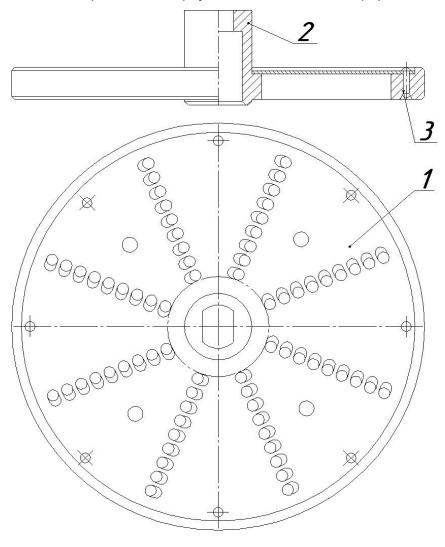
Диск шинковочный: 1 – диск шинковочный, 2 – корпус, 3 – заклепка.
